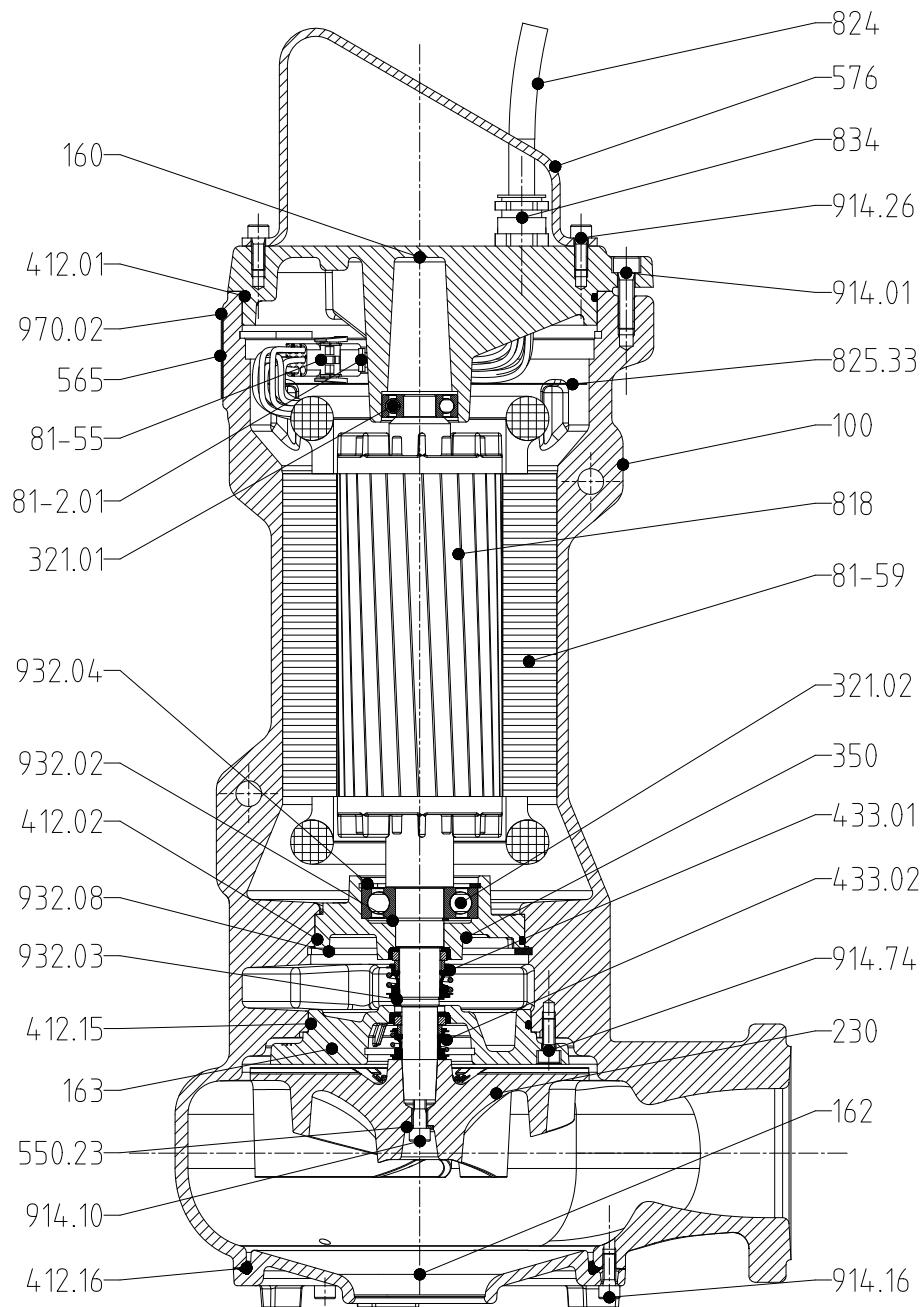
Сборочный чертеж для исполнения US, с рабочим колесом F-max
